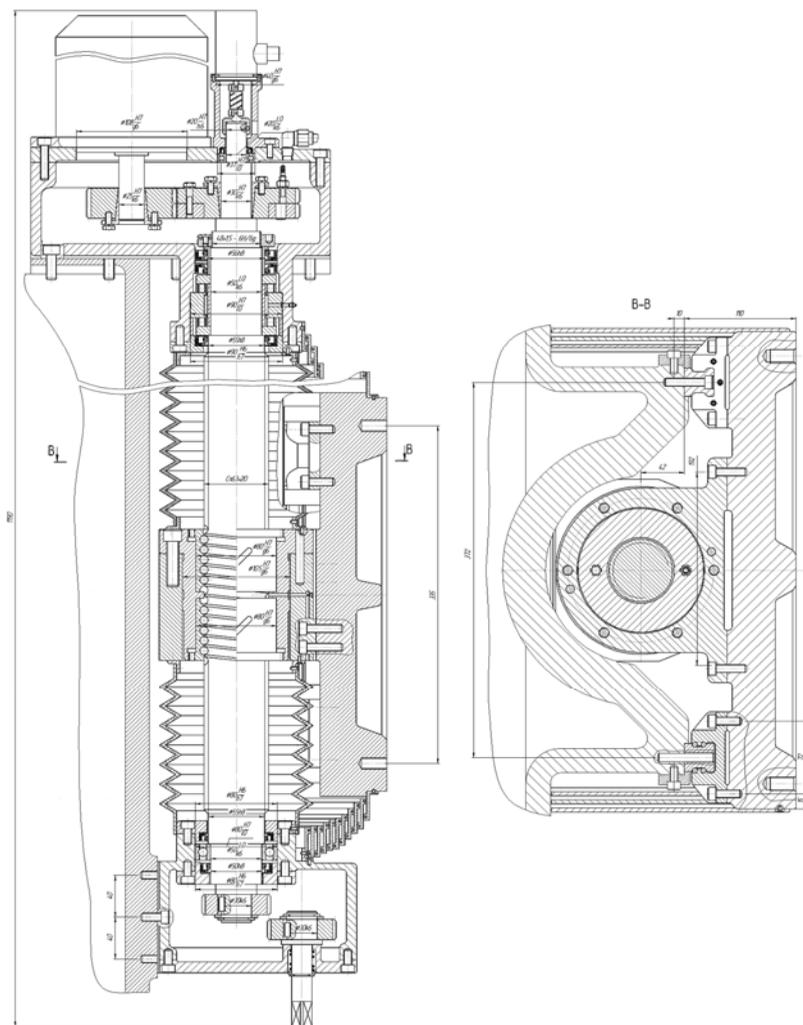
Привод вертикальной подачи шпиндельной бабки многоцелевого станка: с редуктором с беззорной цилиндрической зубчатой передачей; одной фиксирующей опорой ходового винта с комбинированным радиально-упорным роликовым и второй плавающей опорой с радиальным шариковым подшипником; цилиндрическим зубчатым редуктором ручных перемещений; передачей винт-гайка качения с двумя гайками; телескопической защитой направляющих и гармоникообразной ходового винта
